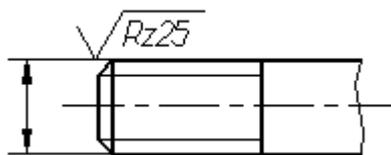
Пример обозначения шероховатости наружной резьбы
